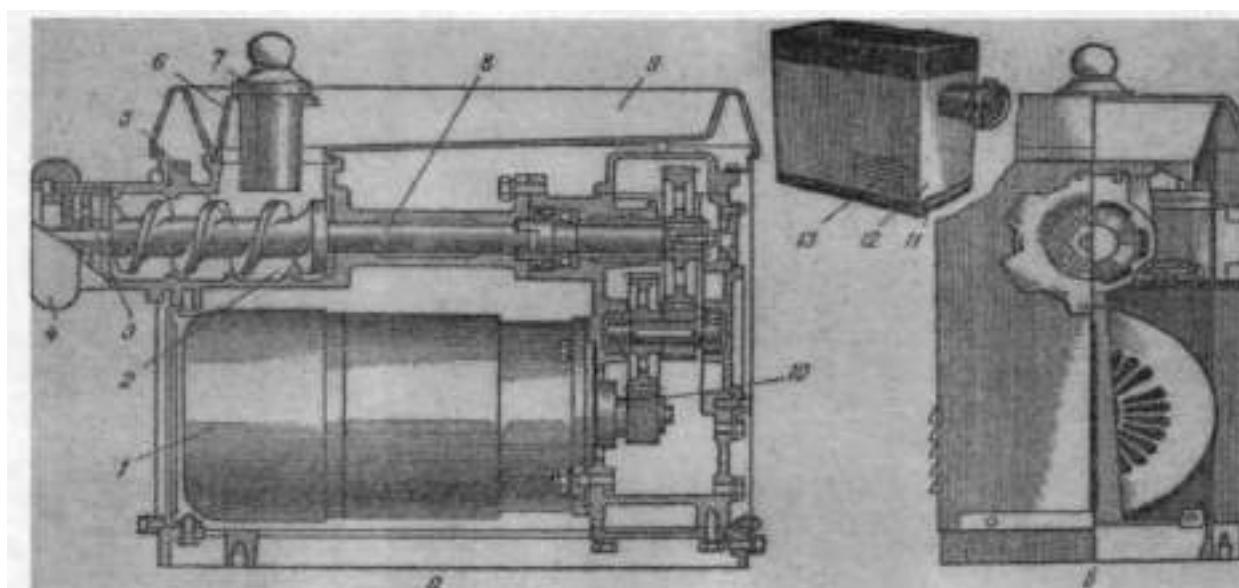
Мясорубка МИМ-82: а - разрез: 1 - электродвигатель; 2 - камера обработки; 3 - палец шнека; 4 - нажимная ганка; 5 - шнек; 6 -
